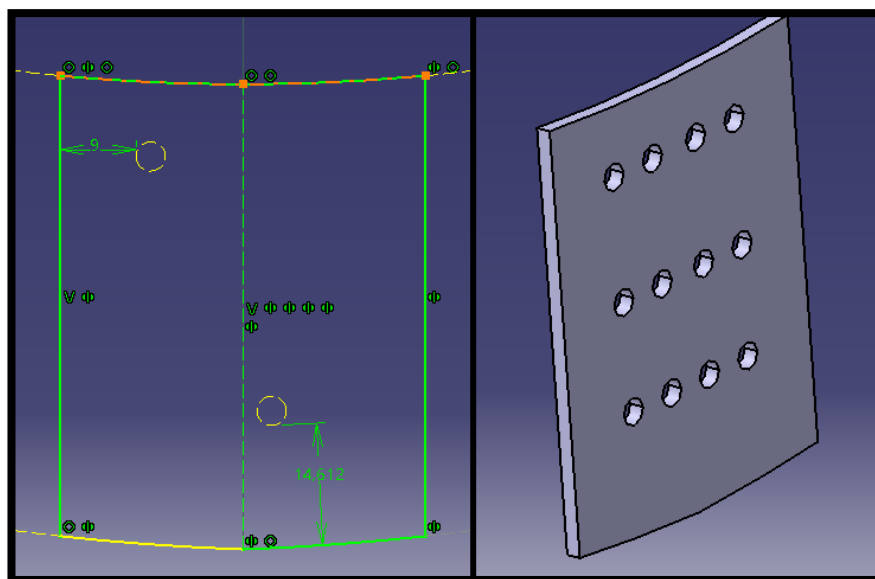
Refuerzo inferior 15: Sketch y pieza final tras extrusión y vaciado
